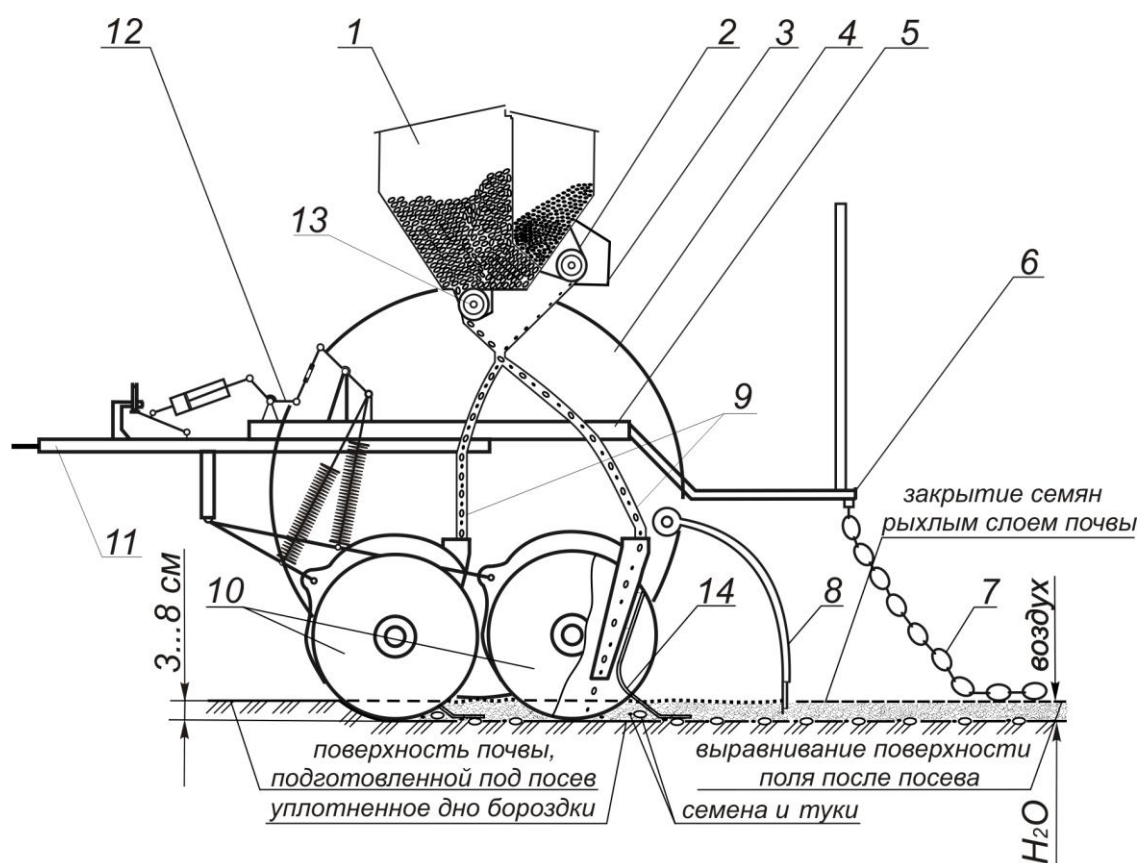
Технологическая схема зерновой сеялки СЗ-3,6 с усовершенствованными двухдисковым сошниками: 1 – зернотуковый ящик; 2 – туковысевающий аппарат; 3 – механизм передачи; 4 – опорно-приводные колеса; 5 – рама; 6 – подножная доска; 7 – цепной шлейф; 8 – загортачи; 9 – семяпроводы; 10 – усовершенствованные сошники, 11 – прицепное устройство; 12 – механизм подъема и опускания сошников; 13 – семявысевающий аппарат; 14 – прижимная пластина
